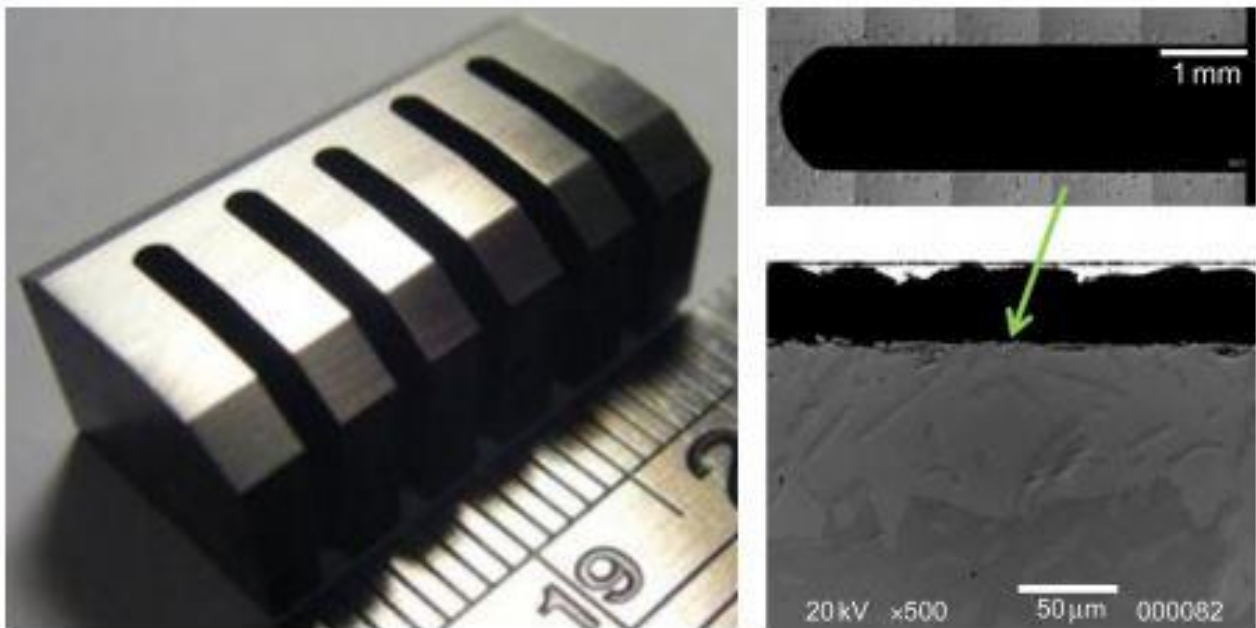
Загартована гребінчаста деталь, та зміцнений поверхневий шар вздовж внутрішньої частини вирізу
